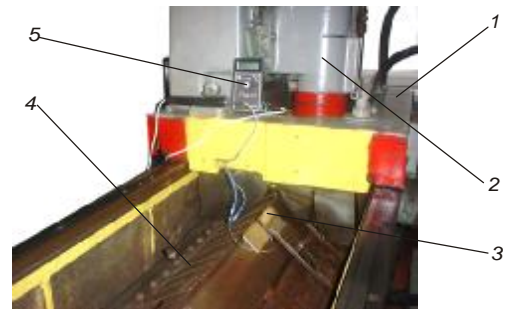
Експериментальна установка: 1 — каретка верстата; 2 — шліфувальна головка; 3 — ніж з термопарою; 4 — поворотний стіл; 5 — цифровий термометр ТТЦ-1-7
